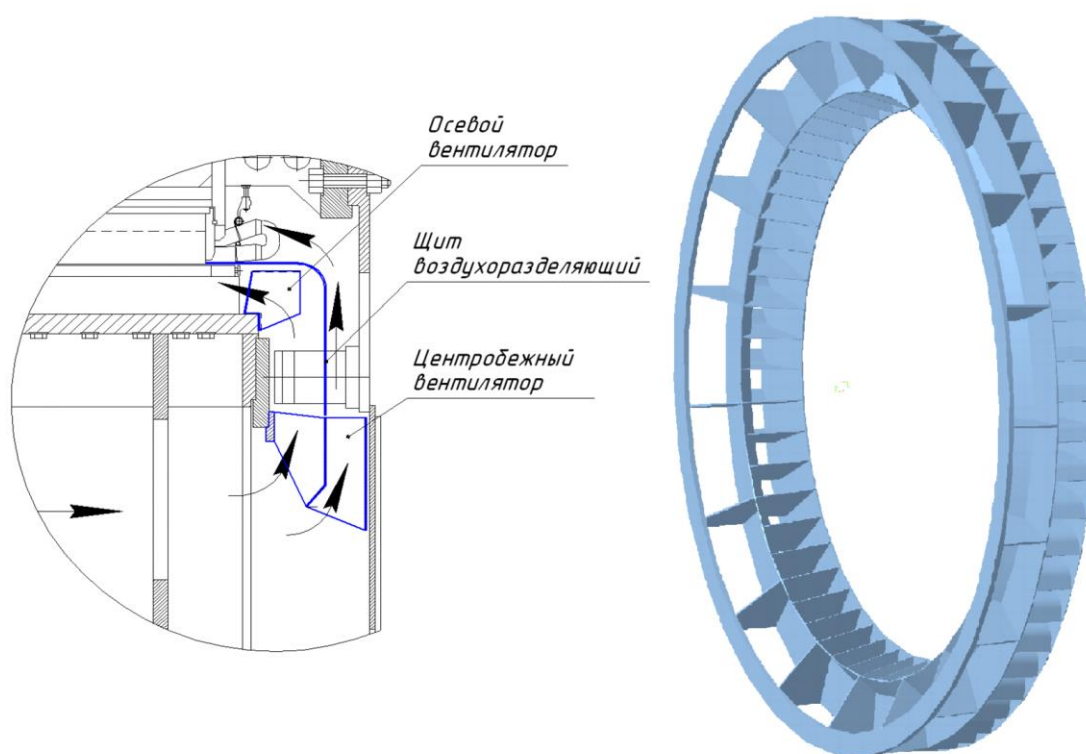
Схема та модель додаткового вентилятора ротора
